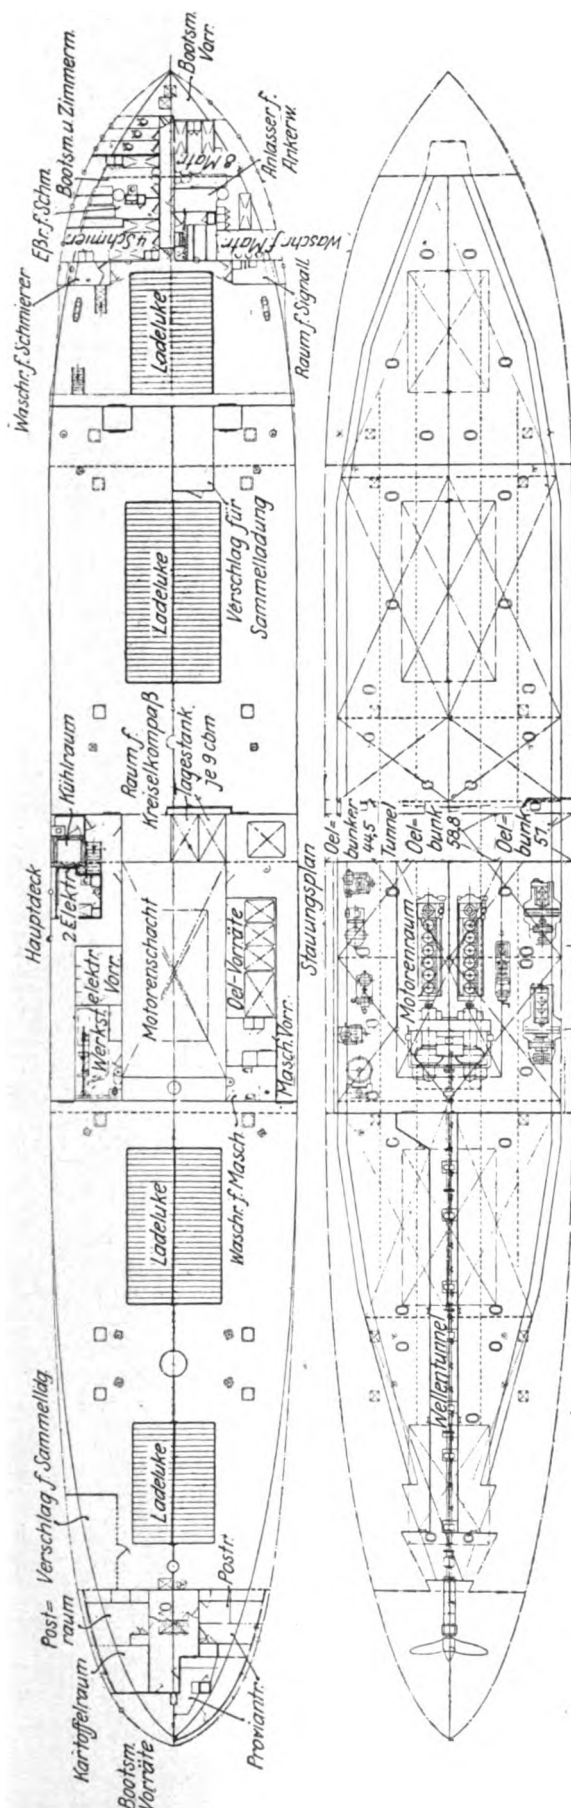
Rotor-Motorschiff „Barbara“, für die Sloman-Linie erbaut von der „Actien-Gesellschaft „Weser“, Bremen
